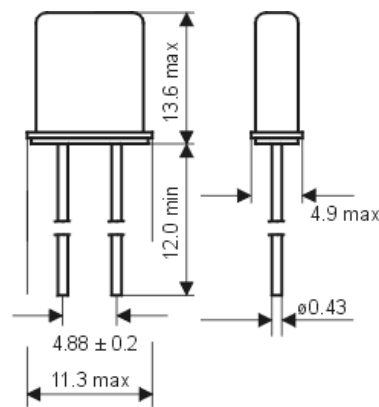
Габаритні розміри кварцового резонатора HC-49S
